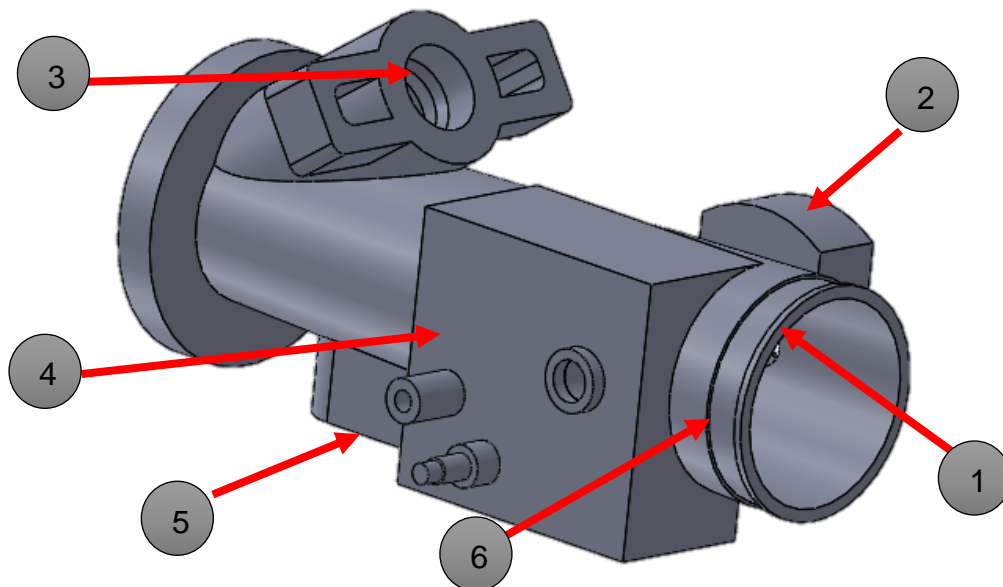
Dimensiones del ducto diseñado en SOLID WORKS
